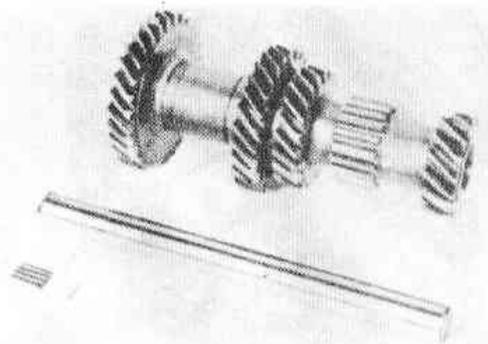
Блок шестерен промежуточного вала коробки передач типа С (Разд. 7)
